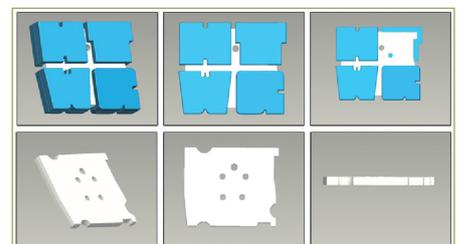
DESIGN DES SCHLÜSSELANHÄNGERS
